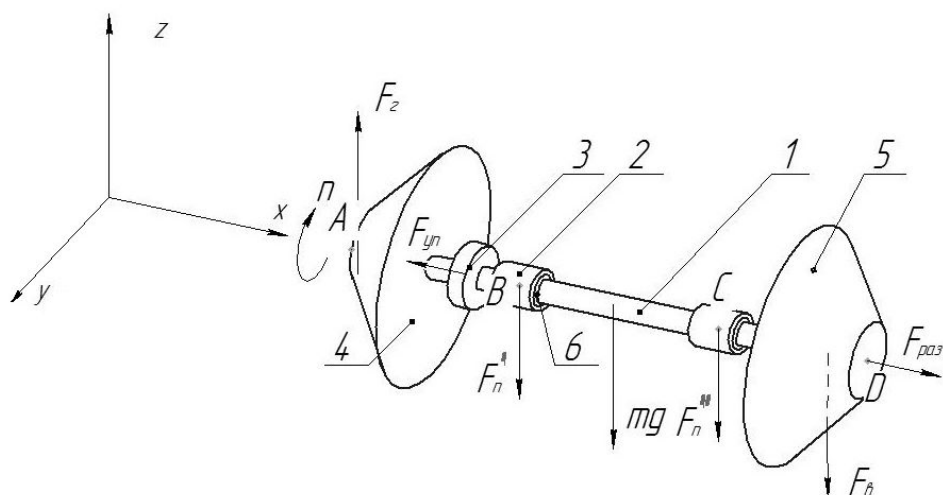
Схема ротора турбокомпрессора с подшипниками
